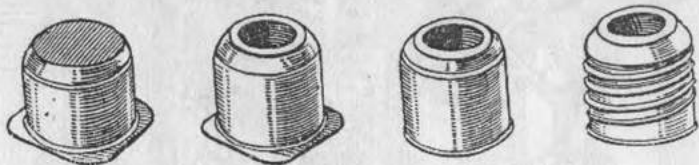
Стадии штамповки цоколей Р27-1.
